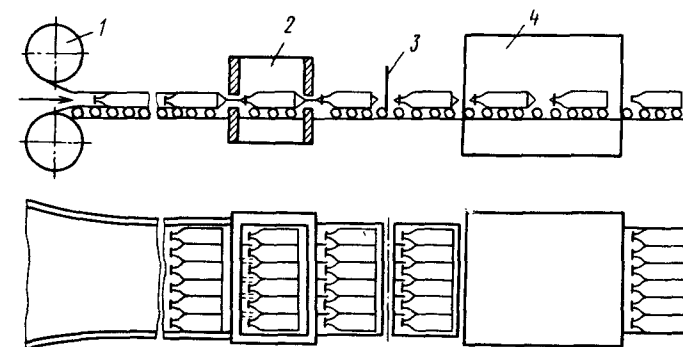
Однорядная упаковка бутылок в термоусадочную пленку: 1 — рулон пленки; 2 — камера сварки; 3 — ножовое устройство; 4 — усадочная камера
